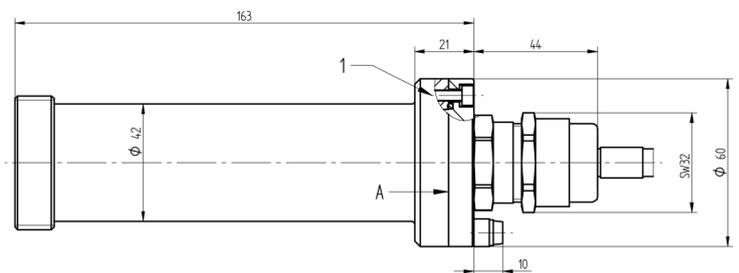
Maßzeichnung Flammenfühler FFS07 für Ex-Zone 1
